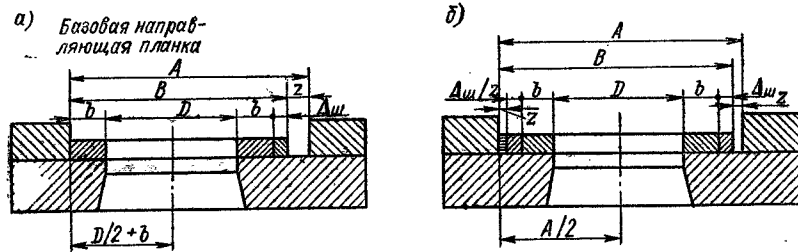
Схемы для подсчета номинальной ширины полосы: а — штамповка с боковым прижимом; б — штамповка без бокового прижима
